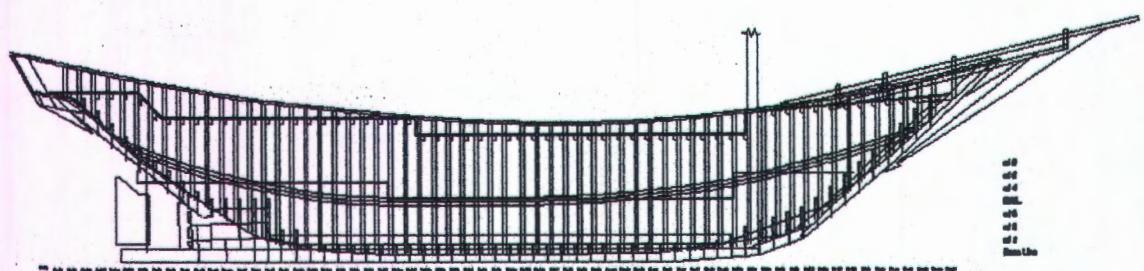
Konstruksi gading (*Frame*) dan wrang (*floor*) dalam bentuk 2 (dua) dimensi.
